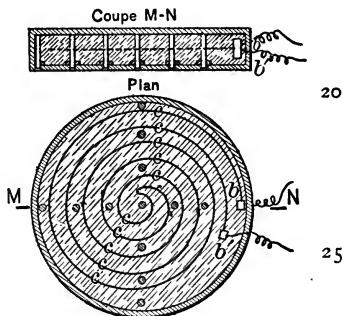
Plaque de fourneau. Vue en plan et en coupe transversale suivant la ligne M N.
